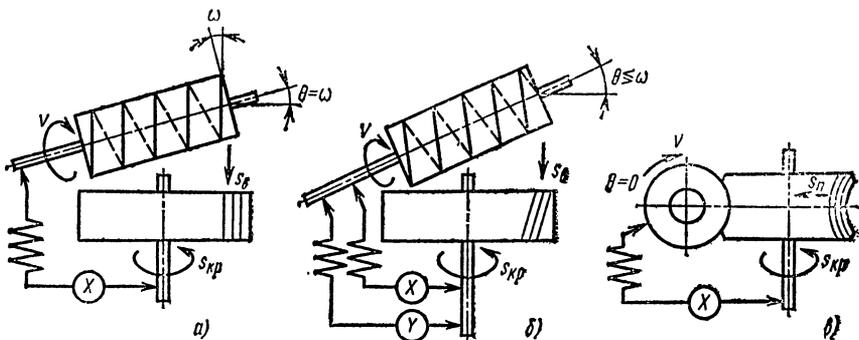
Схемы обработки заготовок на зубофрезерных станках
